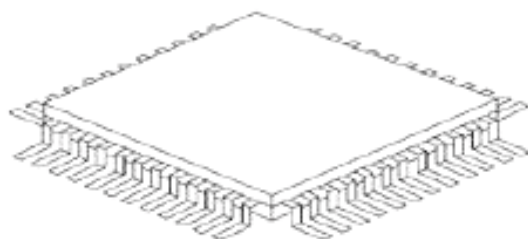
Конструкция корпуса типа PTQFP (квадратного)
